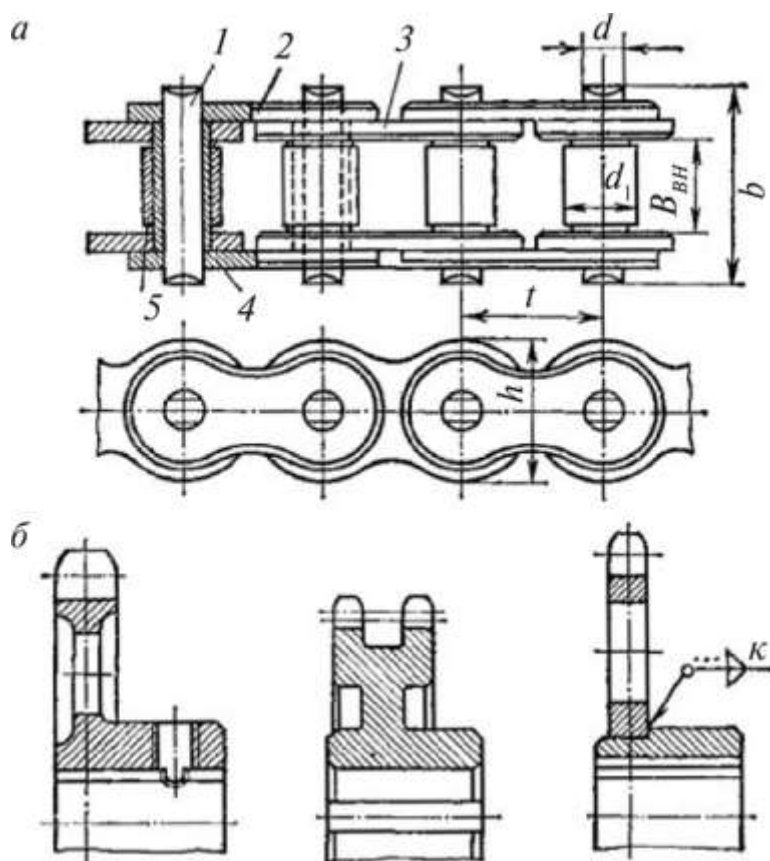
Элементы цепной передачи: *а* — роликовая цепь; *б* — звездочки
